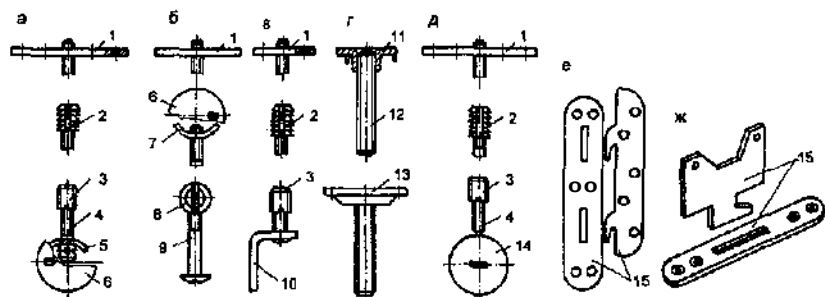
Стяжки мебельные: а-г — резьбовые; д — эксцентриковая; е — клиповая двухкрючковая; ж — клиповая однокрючковая; 1 — гайки-планки; 2 — гайки-тулки с заершением; 3 — гайки-тулки с наружной резьбой; 4 — винты специальные; 5 — шайба-дужка; 6 — заглушка; 7 — ганка-дужка; 8 — гайка цилиндрическая; 9 — винт стандартный; 10 — скоба; 11 — гайка с «усом»; 12 — шпилька; 13 — гайка-фланец; 14 — эксцентрик; 15 — пластины
